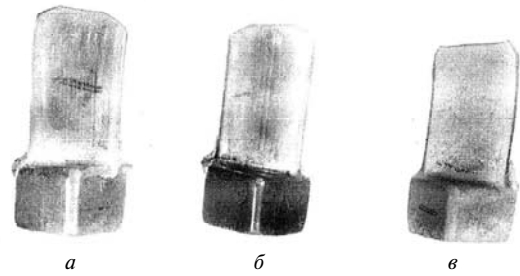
Состояние поверхности заготовки лопатки 7 ступени компрессора с различной толщиной медного покрытия:
